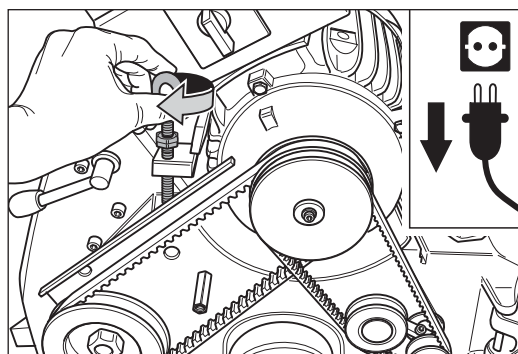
Die beiden Keilriemen auflegen und zum Spannen die Ringschraube am Motor im Uhrzeigersinn drehen.
